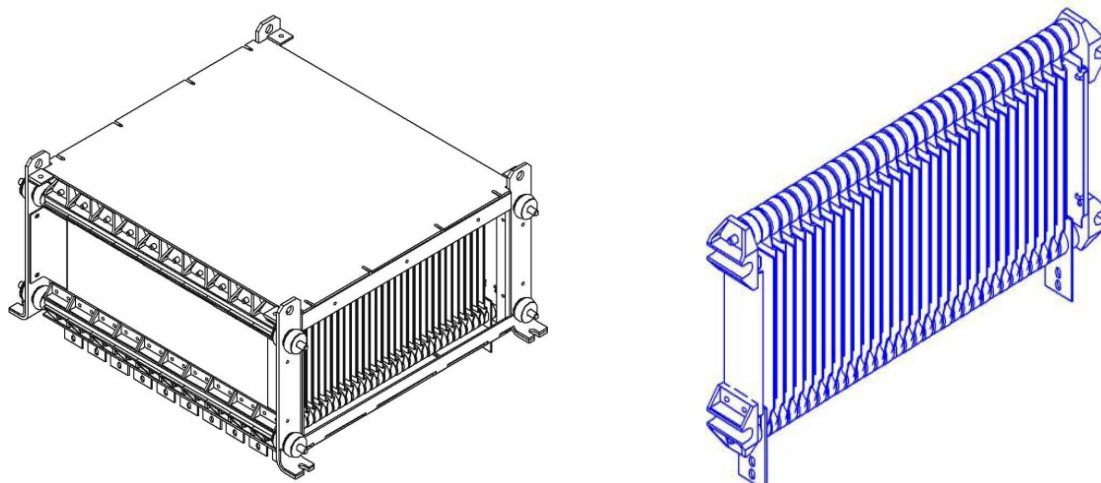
Блок тормозных резисторов. Ленточный резистор РЛТ.
